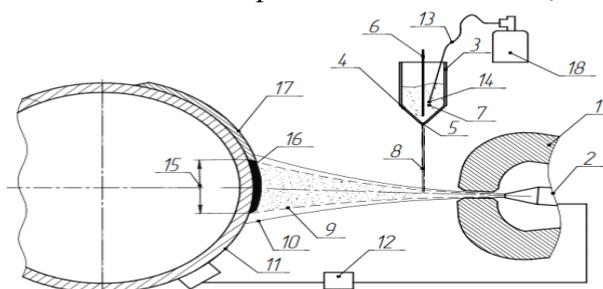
Схема плазменно-порошковой наплавки с внешним вводом порошка в дугу
